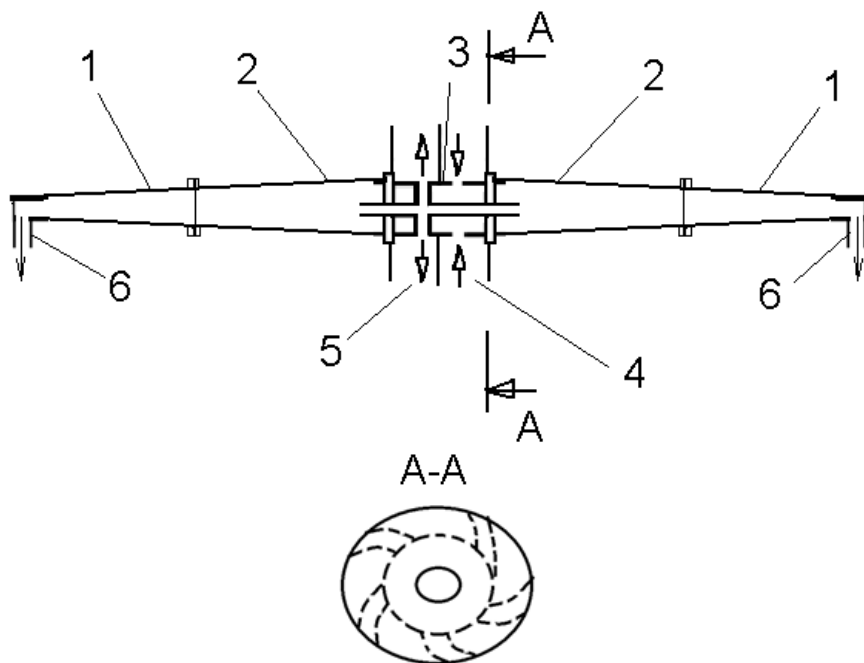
Вихревой очиститель «Twincleaner 132»:
